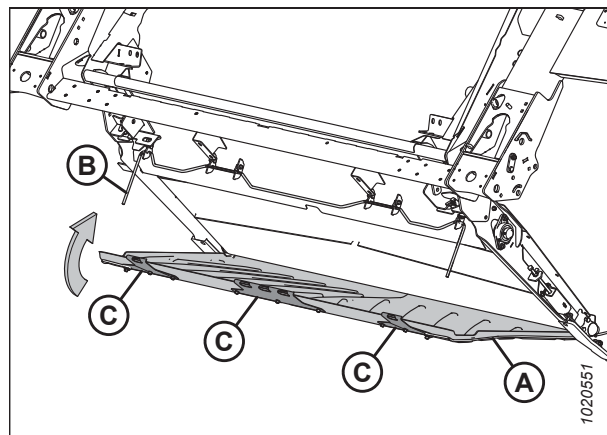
Lado de baixo da janela de inspeção - vista traseira
